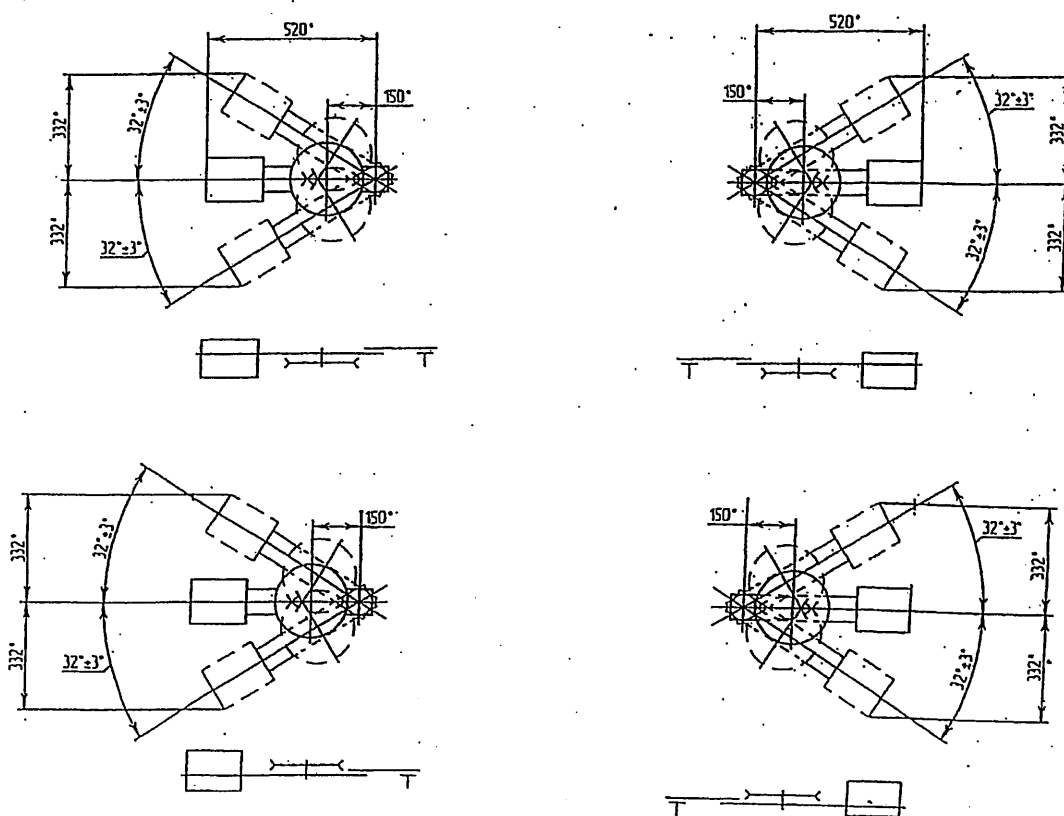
схемы сборки натяжного устройства каната ОС
